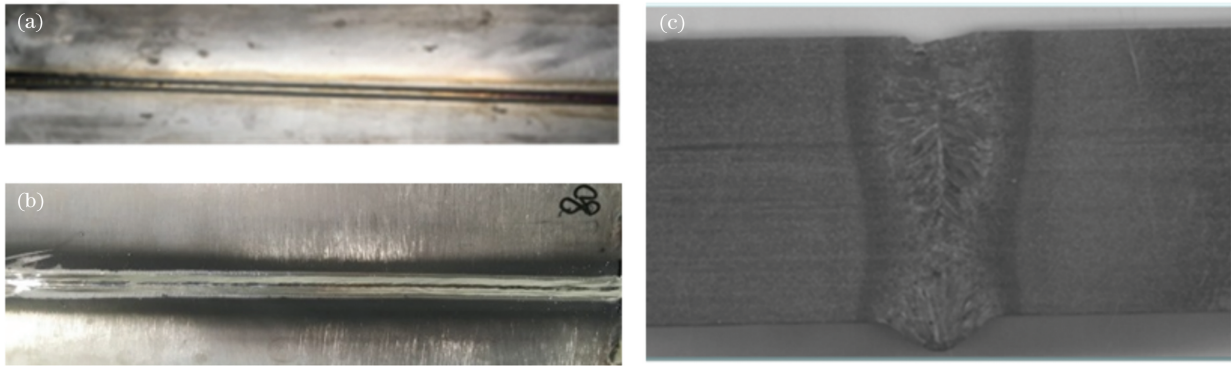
焊接接头的外观形貌。(a)正表面焊缝;(b)背表面焊缝;(c)焊缝横截面的宏观形貌
